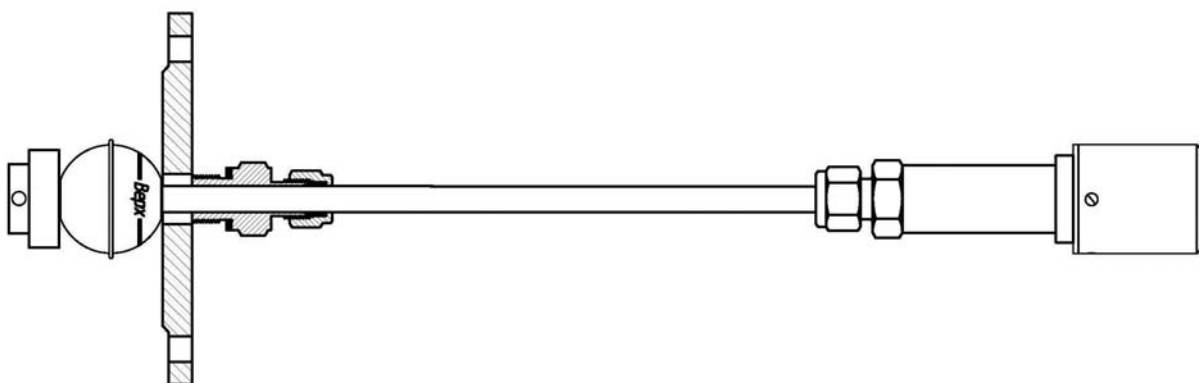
Подготовка уровнемера к монтажу на резервуар
